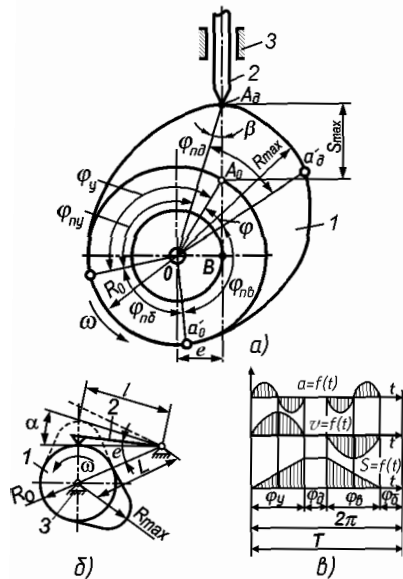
Фазы движения толкателя кулачкового механизма
